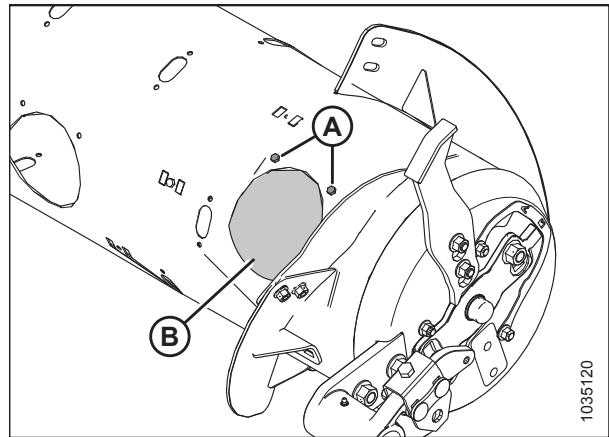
Tampas de acesso do sem fim - Lado direito
